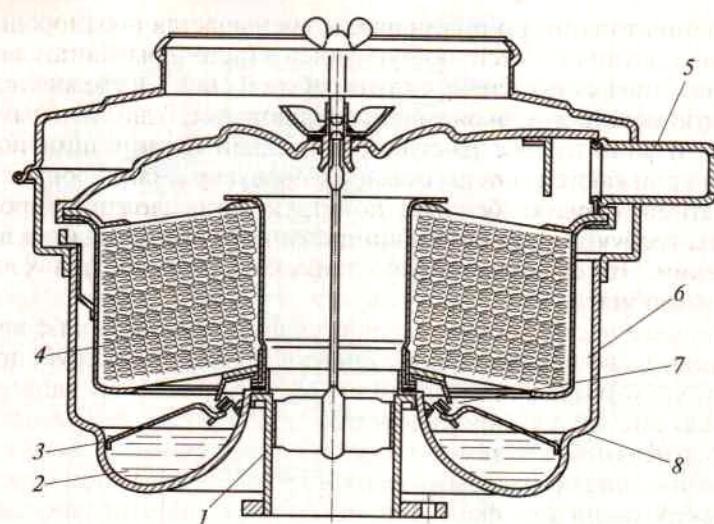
Воздушный фильтр двигателя автомобиля ЗИЛ-4314:
